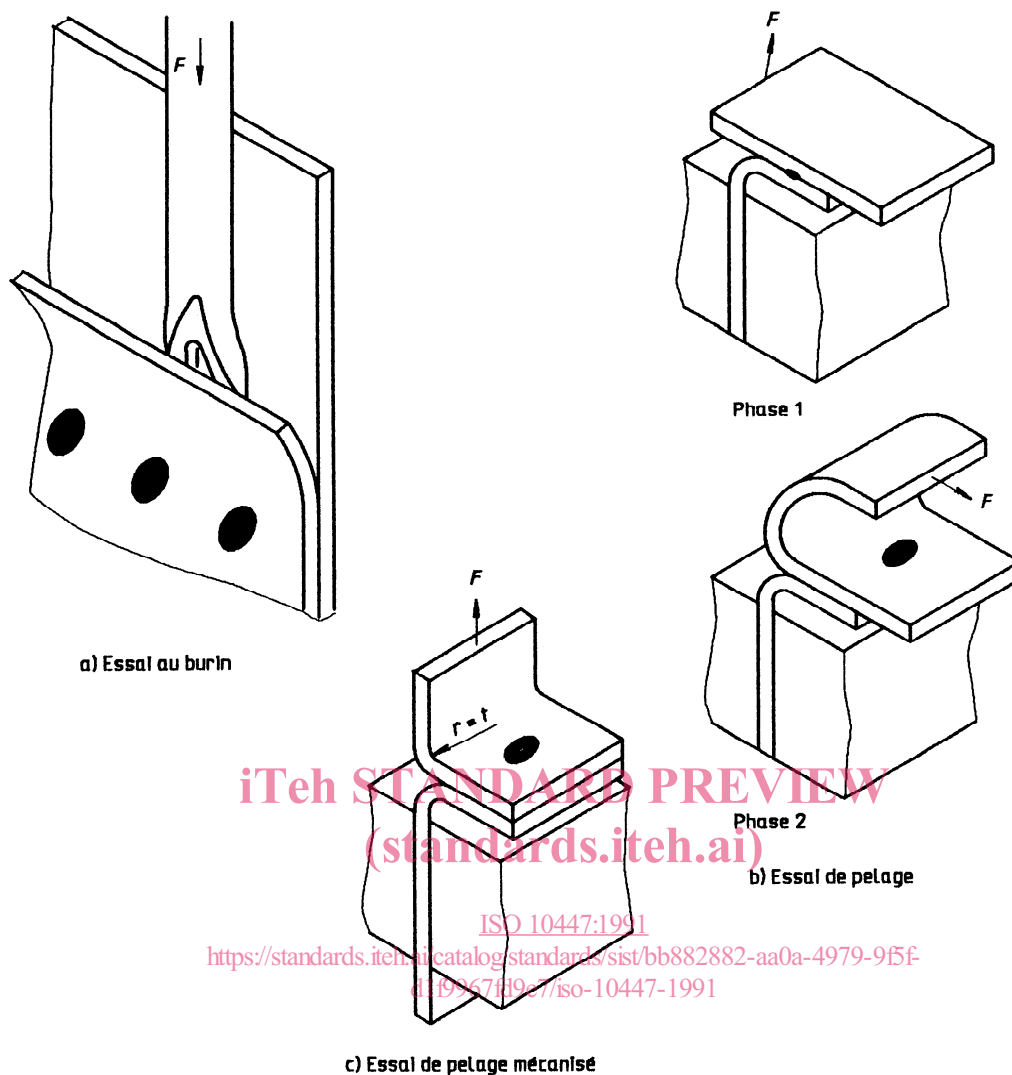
Essais de routine sur assemblage soudé par points
